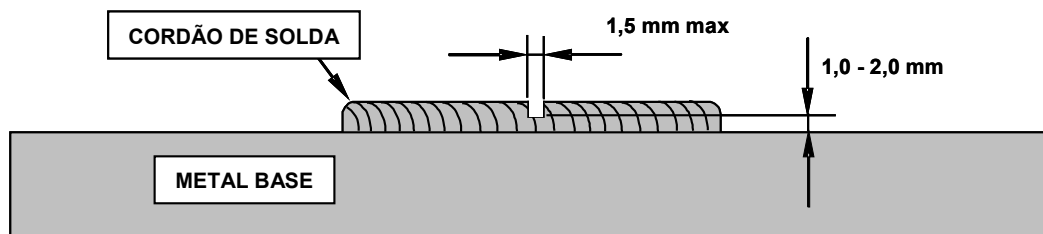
Detalhe do entalhe realizado sobre o cordão de solda depositado no centro do corpo de prova utilizado no ensaio NDT.
